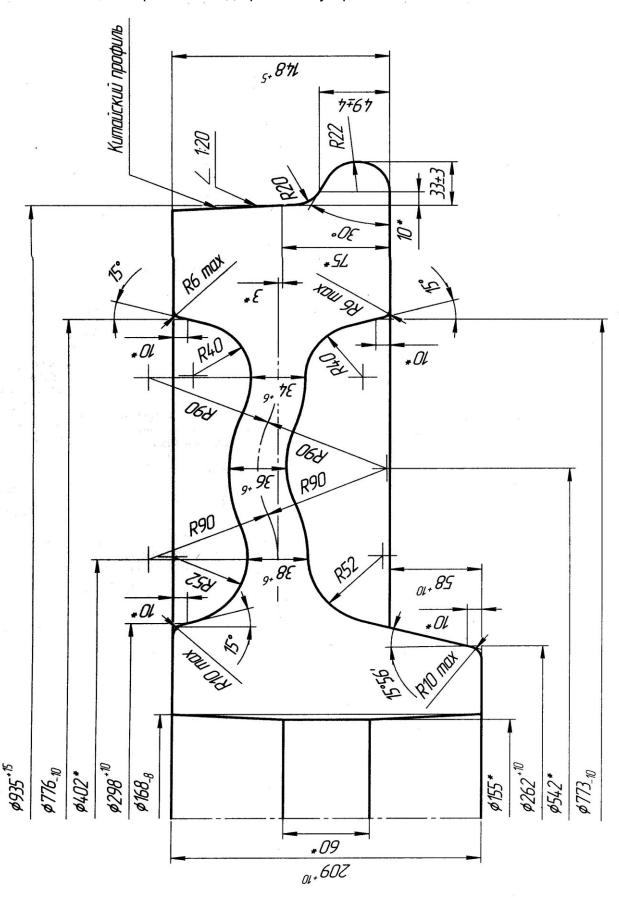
Колесо без механической обработки Ø 935 мм (под чистовое Ø 920 мм, конструкция ВА 409.) Масса чернового колеса 543 кг.
